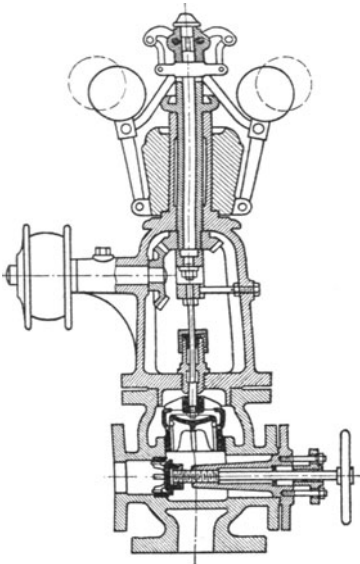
Regulator mit Drosselventil von Steinle & Hartung, Quedlinburg.
